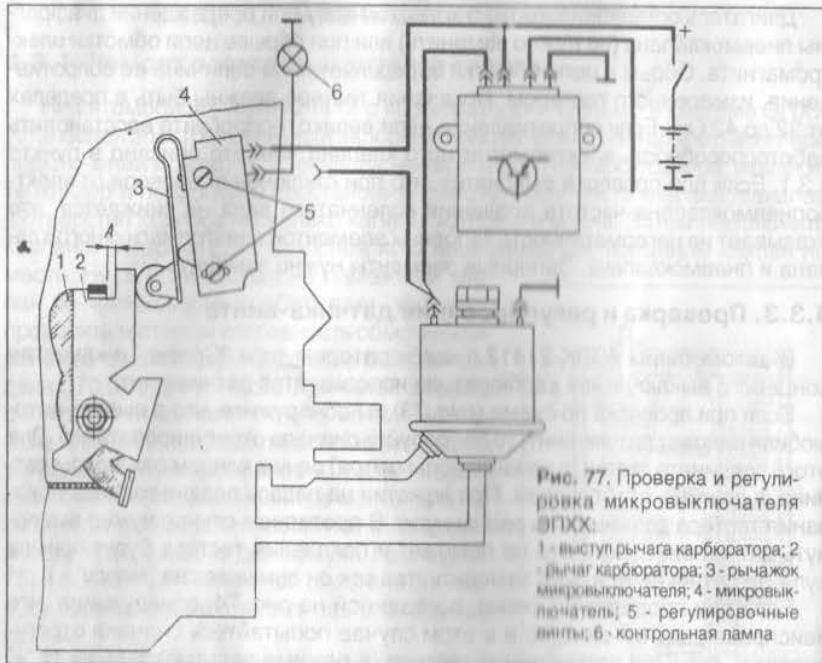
Проверка и регулировка микровыключателя ЭПХХ:
